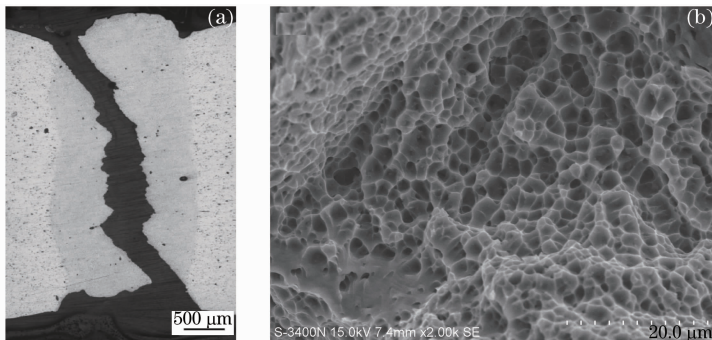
(a) 接头断裂位置; (b) 典型断口形貌
